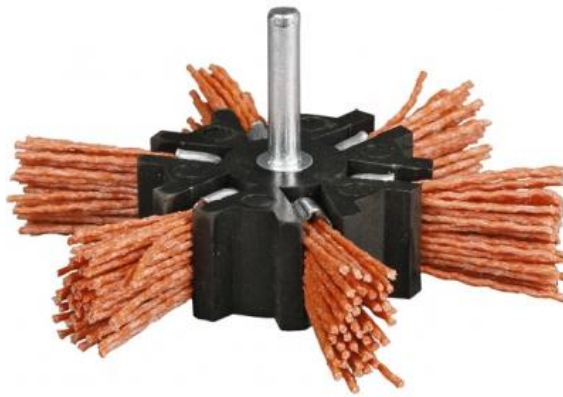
Лепестковые полимерно-абразивные щетки
